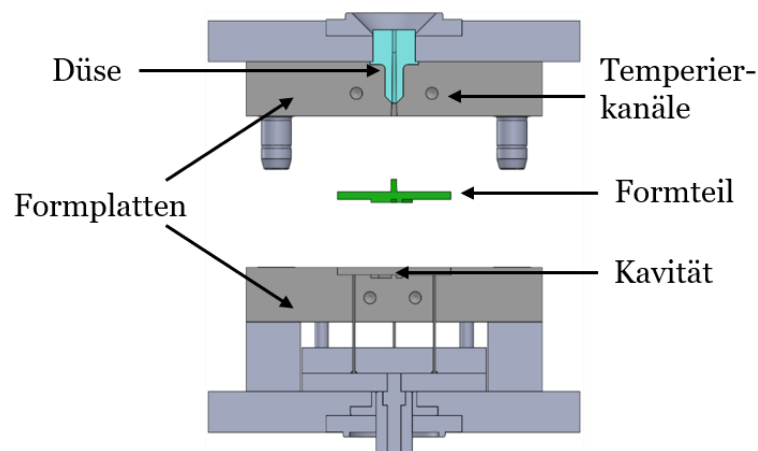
Grundlegender Aufbau eines Spritzgießwerkzeuges im geöffneten Zustand.
